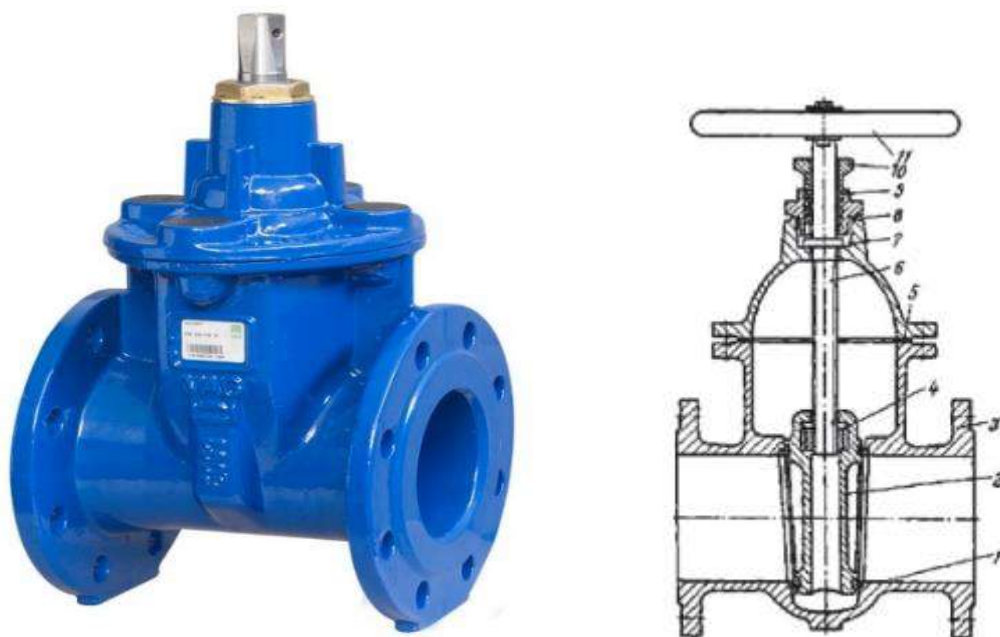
Внешний вид и чертеж клиновой задвижки и ее основные части:
